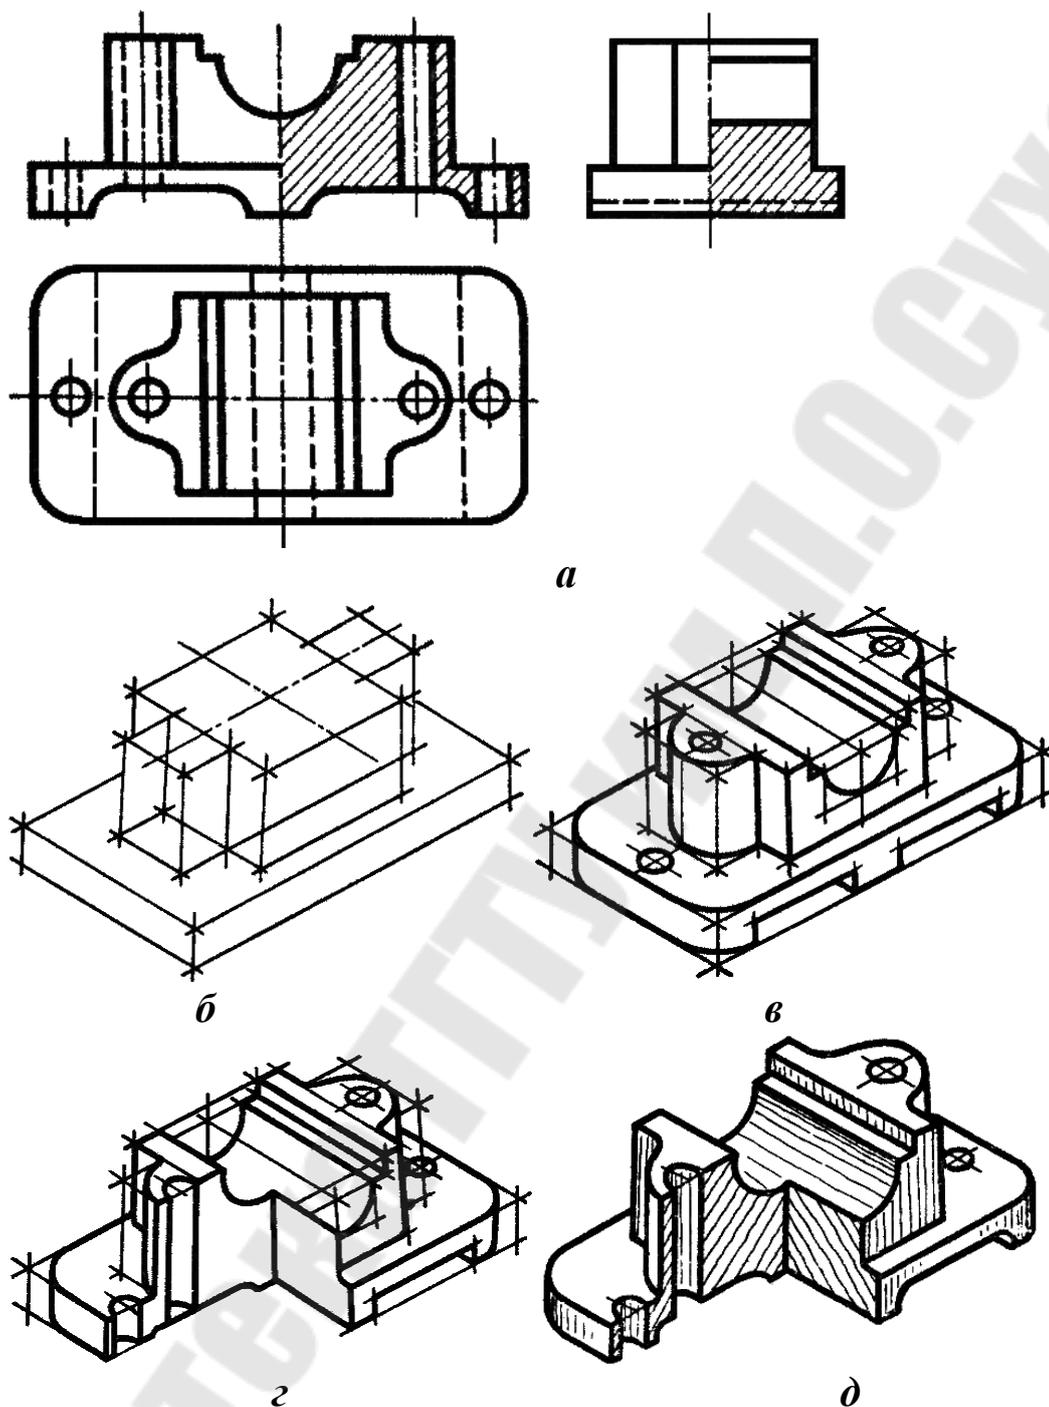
Порядок выполнения рисунка корпуса подшипника
